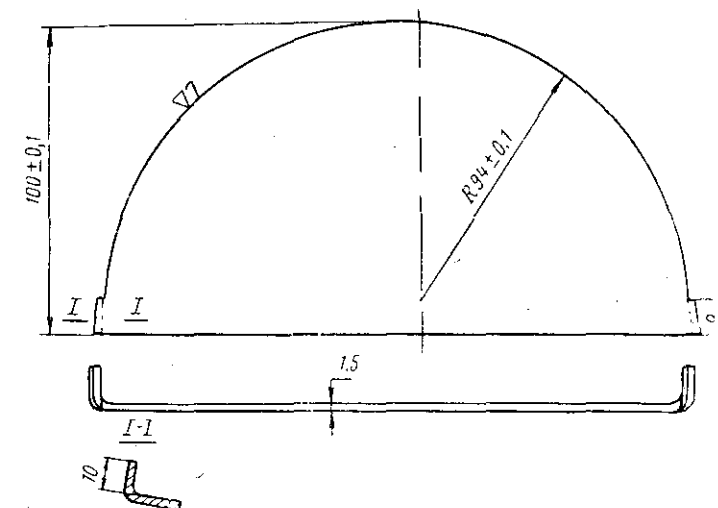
Накладной шаблон 60579/1742 для конца пера лопасти
